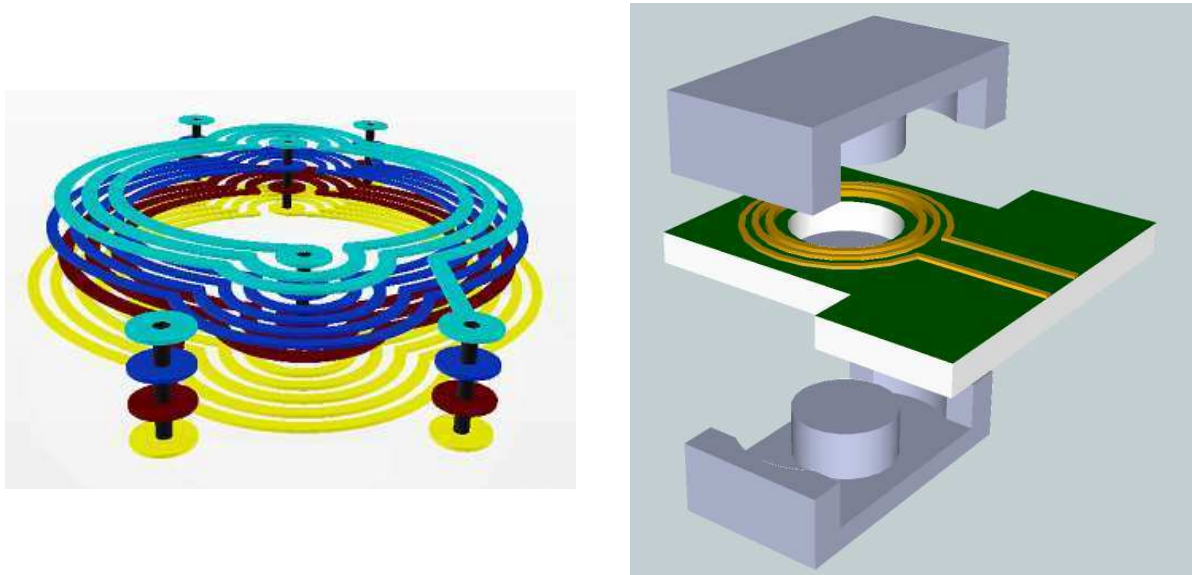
Vue en 3D le transformateur réalisé sur le circuit PCB à 4 couches.
